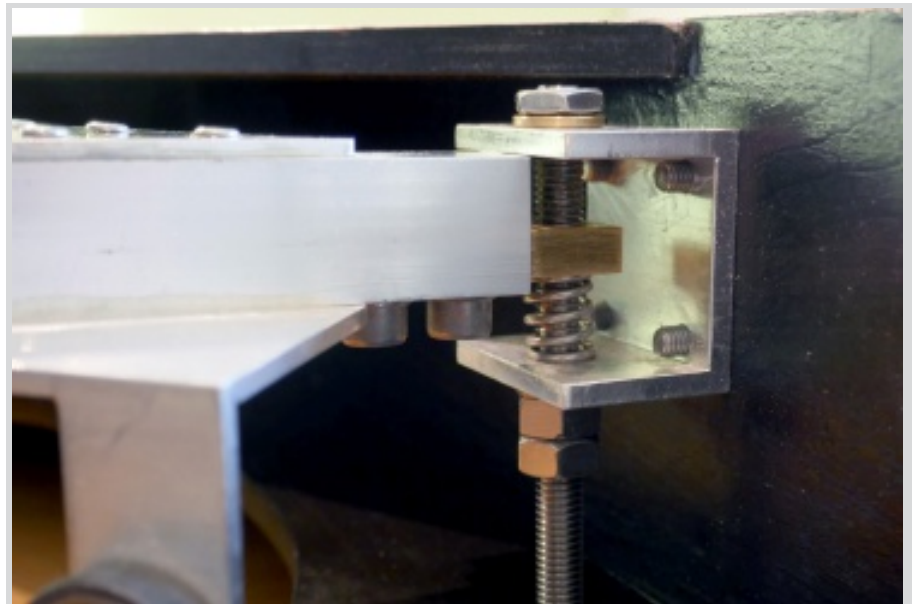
Lagerung des Lagerungsdreiecks mit Messingblock und seiner Verschraubung, sowie die Buchsen der Schraubenlagerung.
